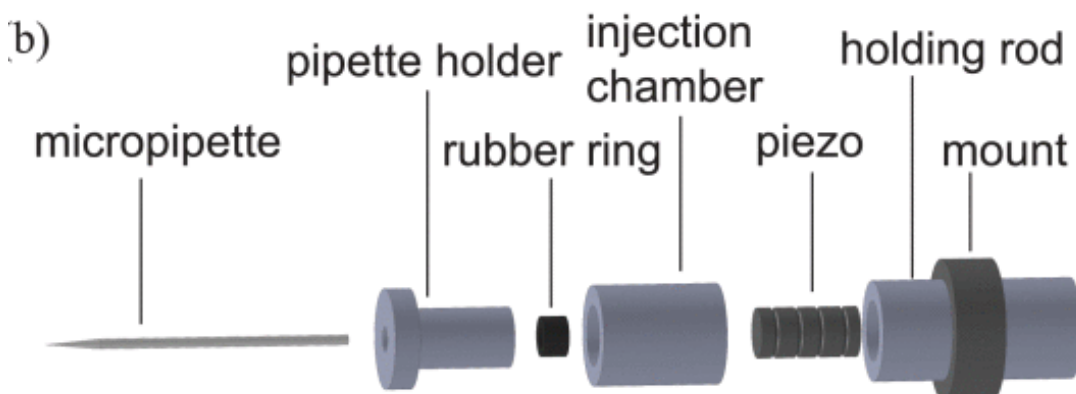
PrimeTech a Burgleigh - umístění piezoaktuátoru
